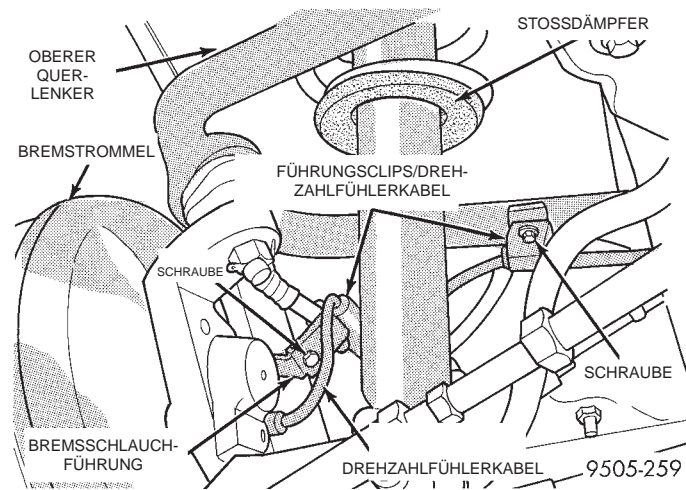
Befestigung des Drehzahlfühlerkabels an der Hinterradaufhängung
